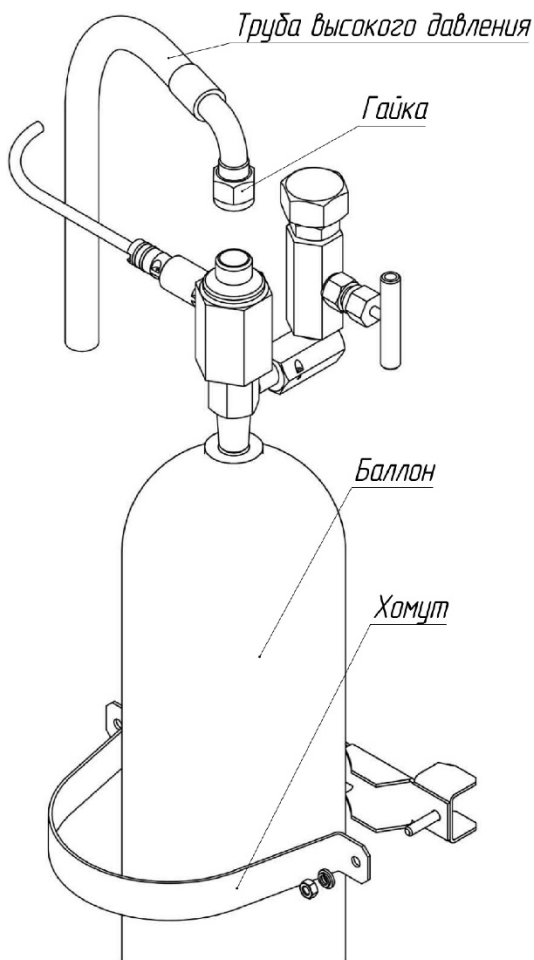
Внешний вид блока рабочего газа «БРГ-10».
